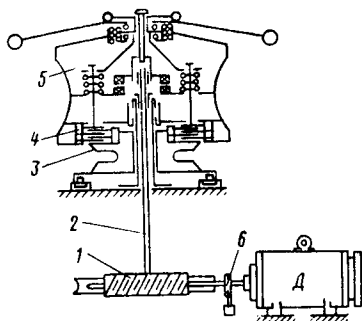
Кинематическая схема якорно-швартовного шпиля.
